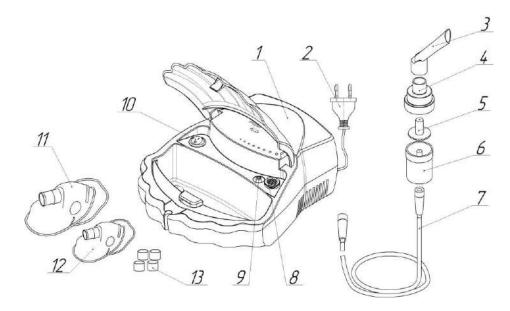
1 — блок компрессорный, 2 — шнур электропитания с вилкой, 3 — штуцер, 4 — крышка камеры распылительной, 5 — втулка распылительная, 6 — корпус камеры распылительной, 7 — шланг, 8 — заглушка, 9 — разъем для шланга, 10 — выключатель, 11 — маска для взрослых, 12 маска для детей, 13 —фильтр.
